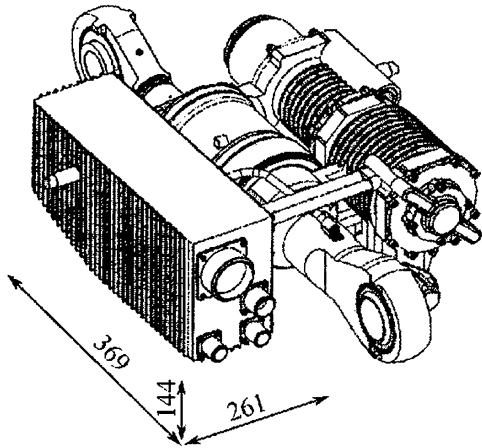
Внешний вид электрогидростатического привода поворота руля самолета и его габаритные размеры
